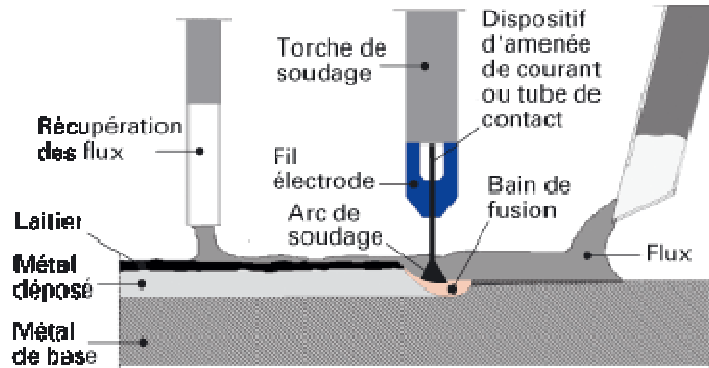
procédé automatique de soudage sous flux solide en poudre [TIC25]
